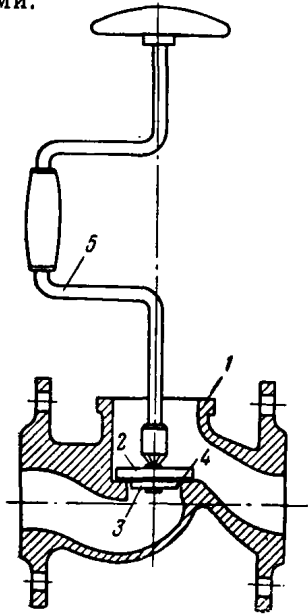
Приспособление для шлифовки вентилей Ду 50 мм:
